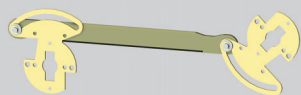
РАЗМЕРЫ см. стр. Н22
